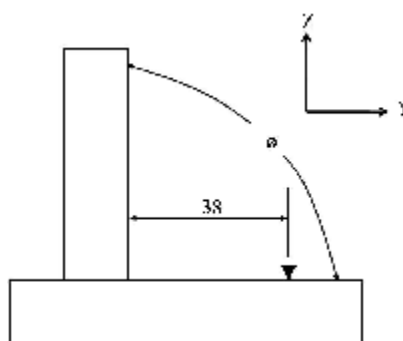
Medição do ângulo da junta após a soldagem (junta livre).
